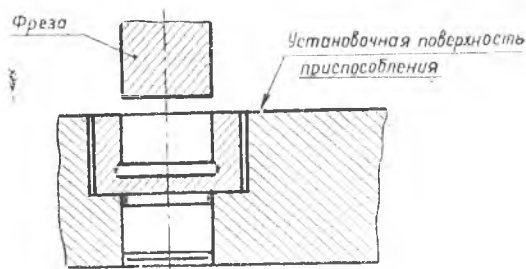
Настроечный элемент для фрезы в приспособлении для установки и закрепления детали
